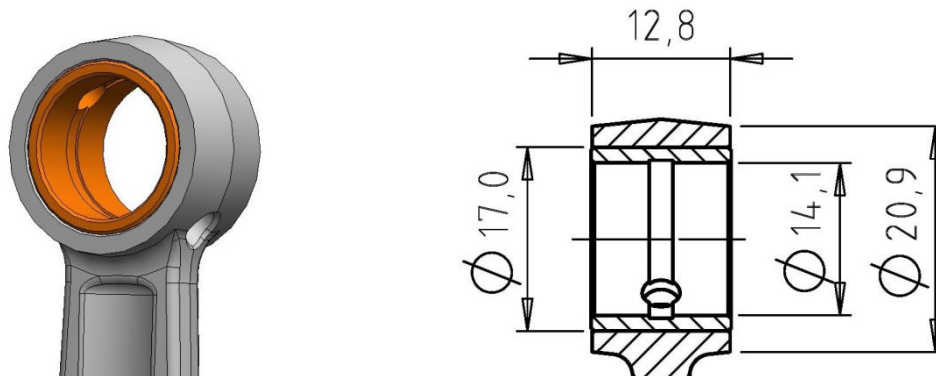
Hlavní rozměry ojnice motoru Jawa 50 typ 223.200
